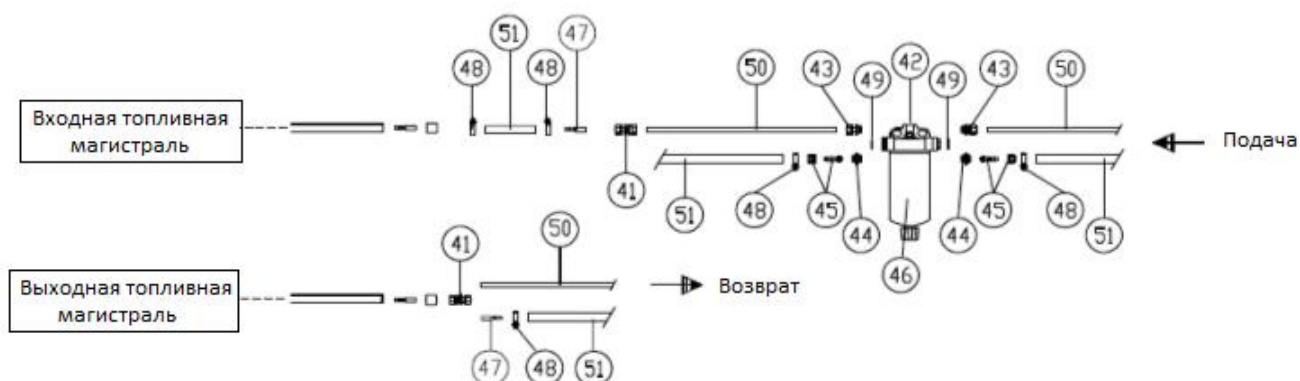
Монтажные приспособления для набора деталей для подачи топлива
